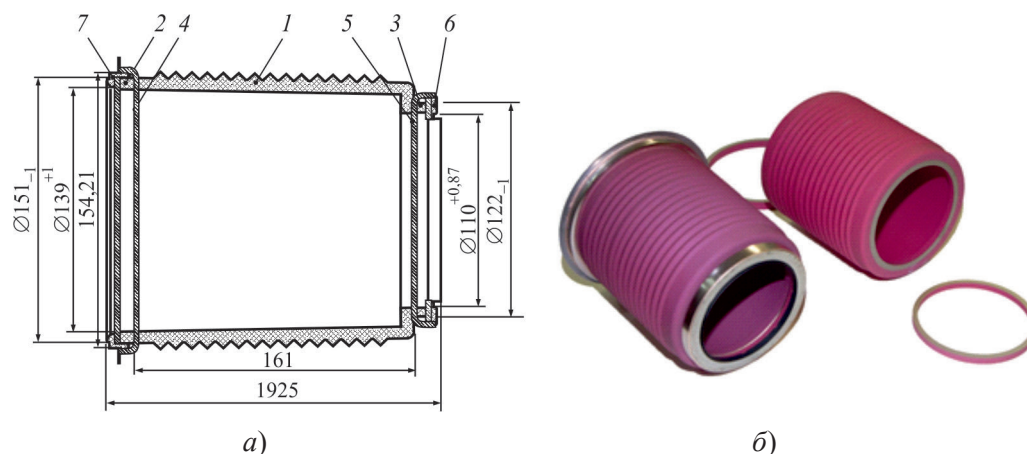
Чертеж (а) и фотография (б) изготовленного высоковольтного металлокерамического изолятора
